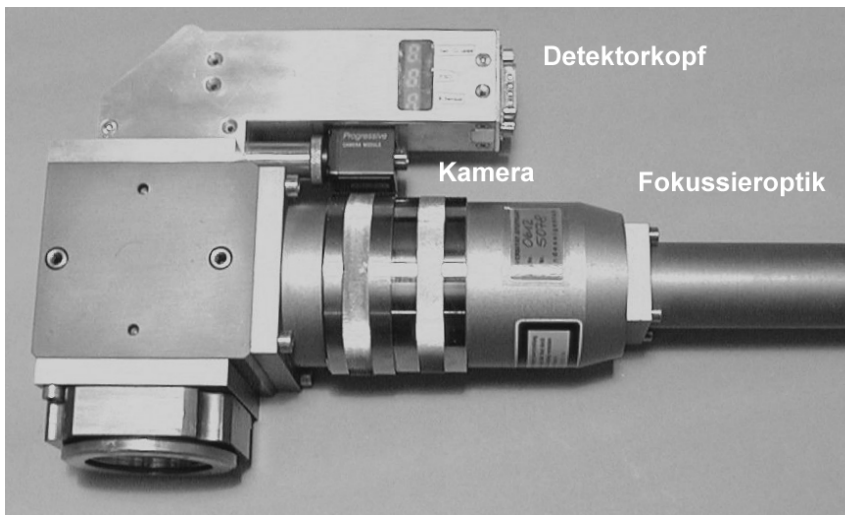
Detektorsystem mit Kamera und Bearbeitungskopf für das Laserstrahlschweißen mit Nd:YAG-Laser.
